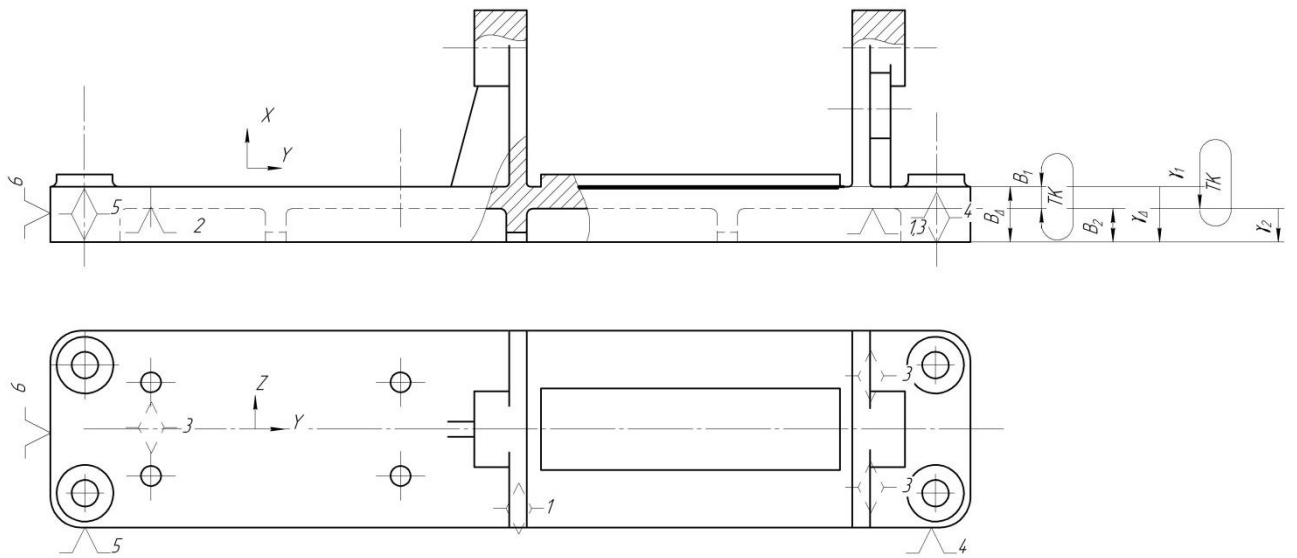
Другий варіант базування станини при обробці поверхні під корпус
